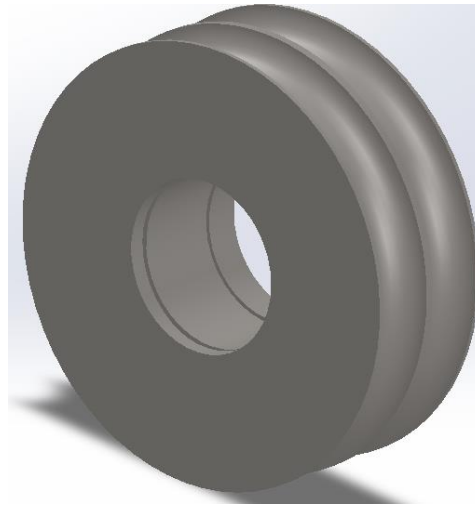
Vista de pieza N°12 (Fuente 100)
